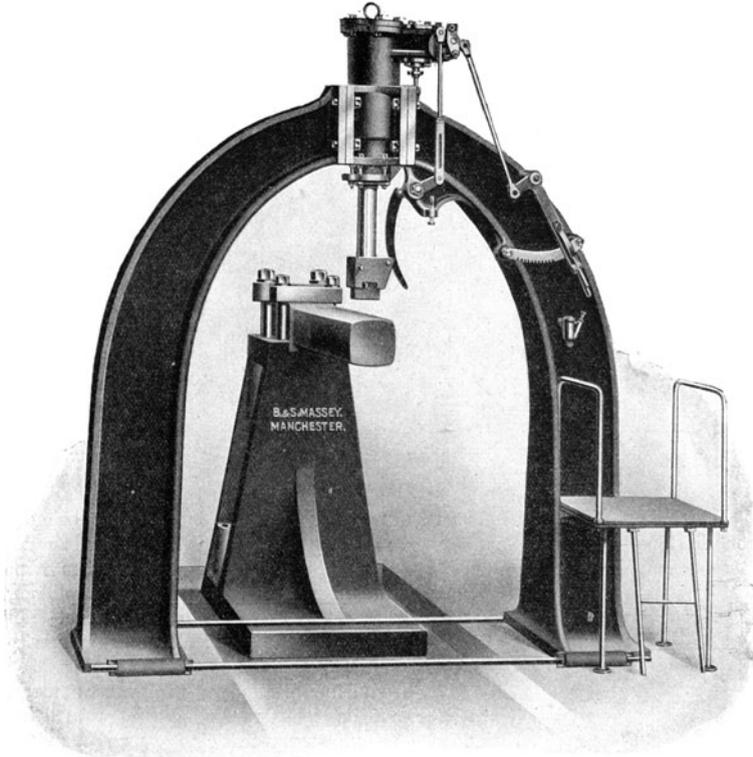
Hämmer zum Schweißen von Röhren. Bogenform ohne Führungen. Von Massey in Manchester.
